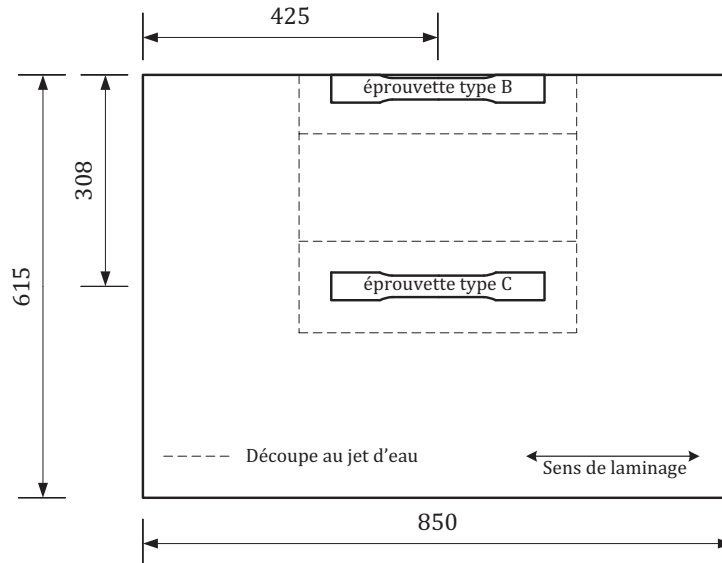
Emplacement des éprouvettes testées (en mm).
